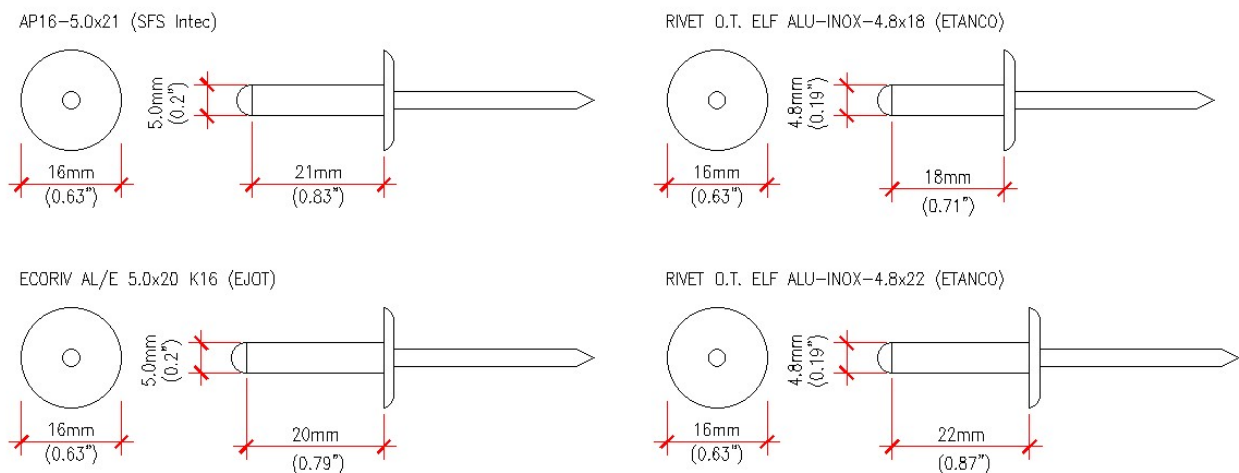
Rebites para fixação dos painéis Viroc em estrutura metálica
